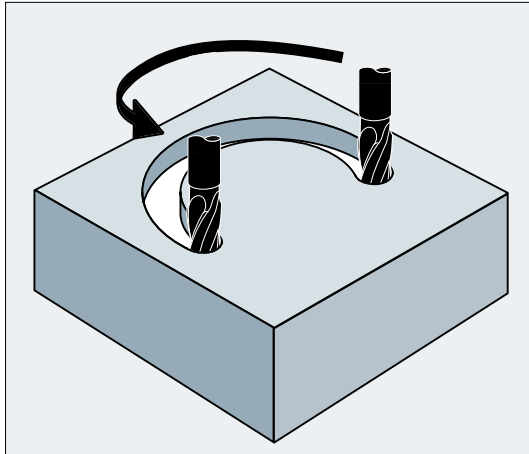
Пример использования: Фрезерование кругового паза
